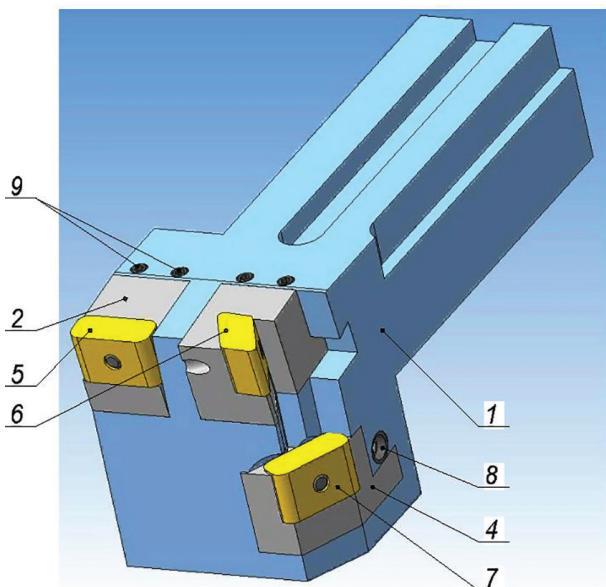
Предлагаемая конструкция резца для обточки колесных пар повышенной твердости:
